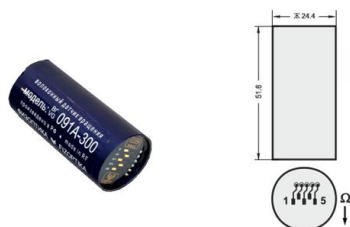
Общий вид и габаритный чертеж ВГ 091А-300
